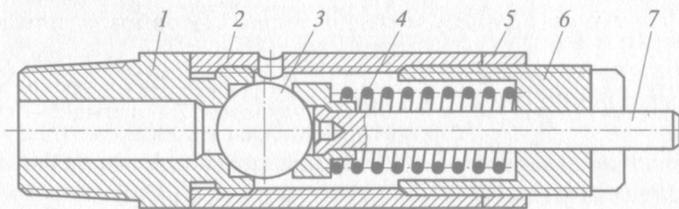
Предохранительный клапан пневматического тормозного привода автомобиля ЗИЛ-130:
